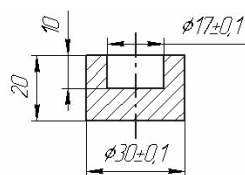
Порошковая деталь, полученная выдавливанием пористой заготовки
